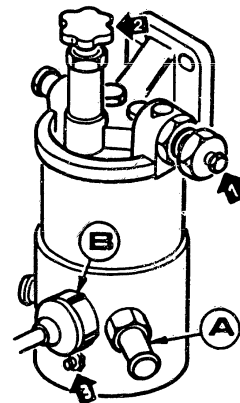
Feinfilter Roto-Diesel. Der Filter inklusive Dichtung muss alle 22500km ersetzt werden. 1 Entlüfterschraube – 2 Handpumpe – 3 Wasserablassschraube – A = Thermostat, regelt Wassertemperatur auf ca. 35°C – B = Wassergehaltsanzeige.
